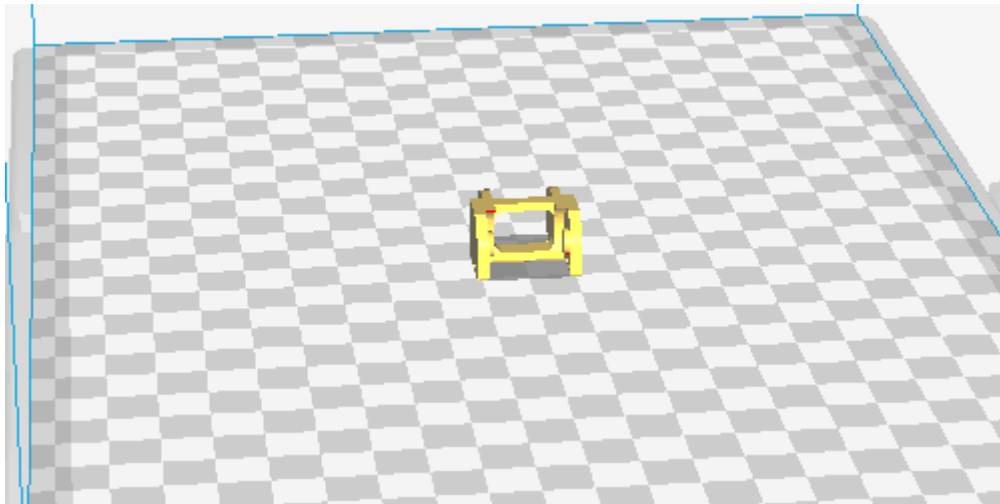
Posición de impresión de una de las piezas que forma el conjunto de la cadena portacable 2.
